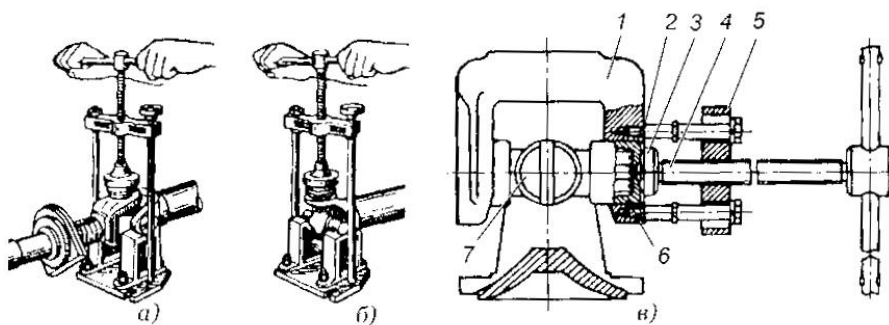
Разборка карданного шарнира с помощью универсального съемника: а — выпрессовка подшипников из скользящей вилки; б — выпрессовка подшипников из вилки карданного вала; в — разборка карданного вала автомобиля марки «КамАЗ»; 1 — вилка; 2 — установочный болт; 3 — пята; 4 — винт съемника; 5 — поперечина; 6 — стакан; 7 — крестовина
